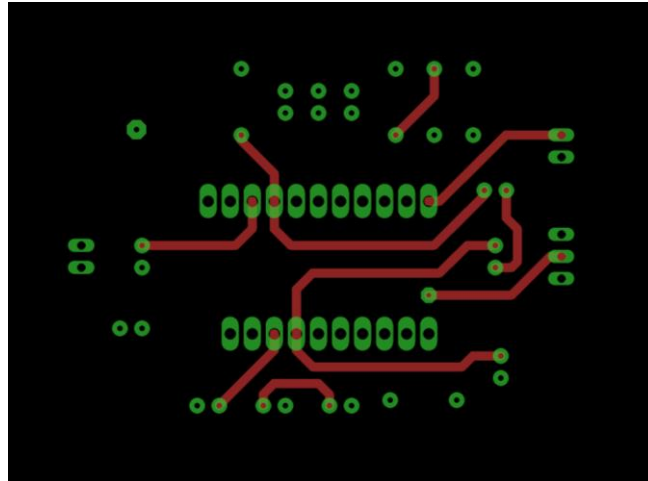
PCB del circuito para el chip bq51050B (TOP)
